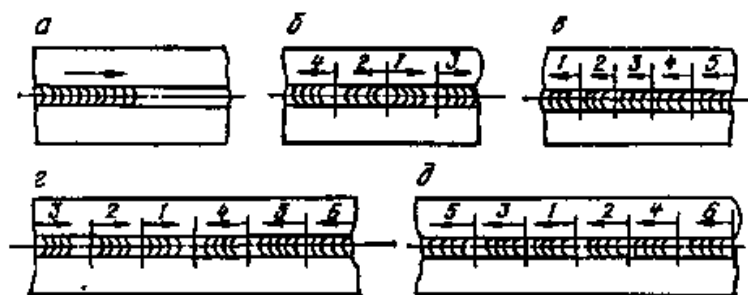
Схемы наложения сварных швов различной длины разными способами (номера указывают последовательность выполнения швов):
